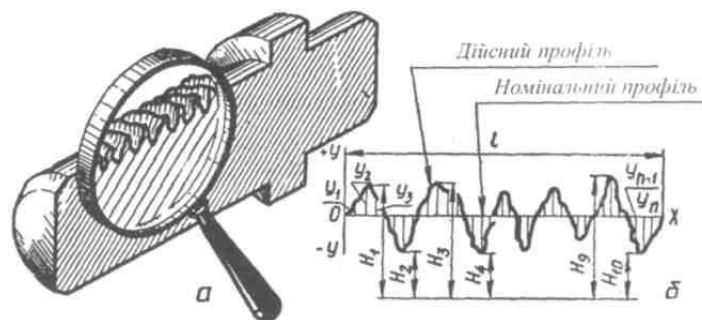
Мікронерівності на поверхні деталі після механічної обробки: а - загальний вигляд; б - схема кількісного оцінювання.
